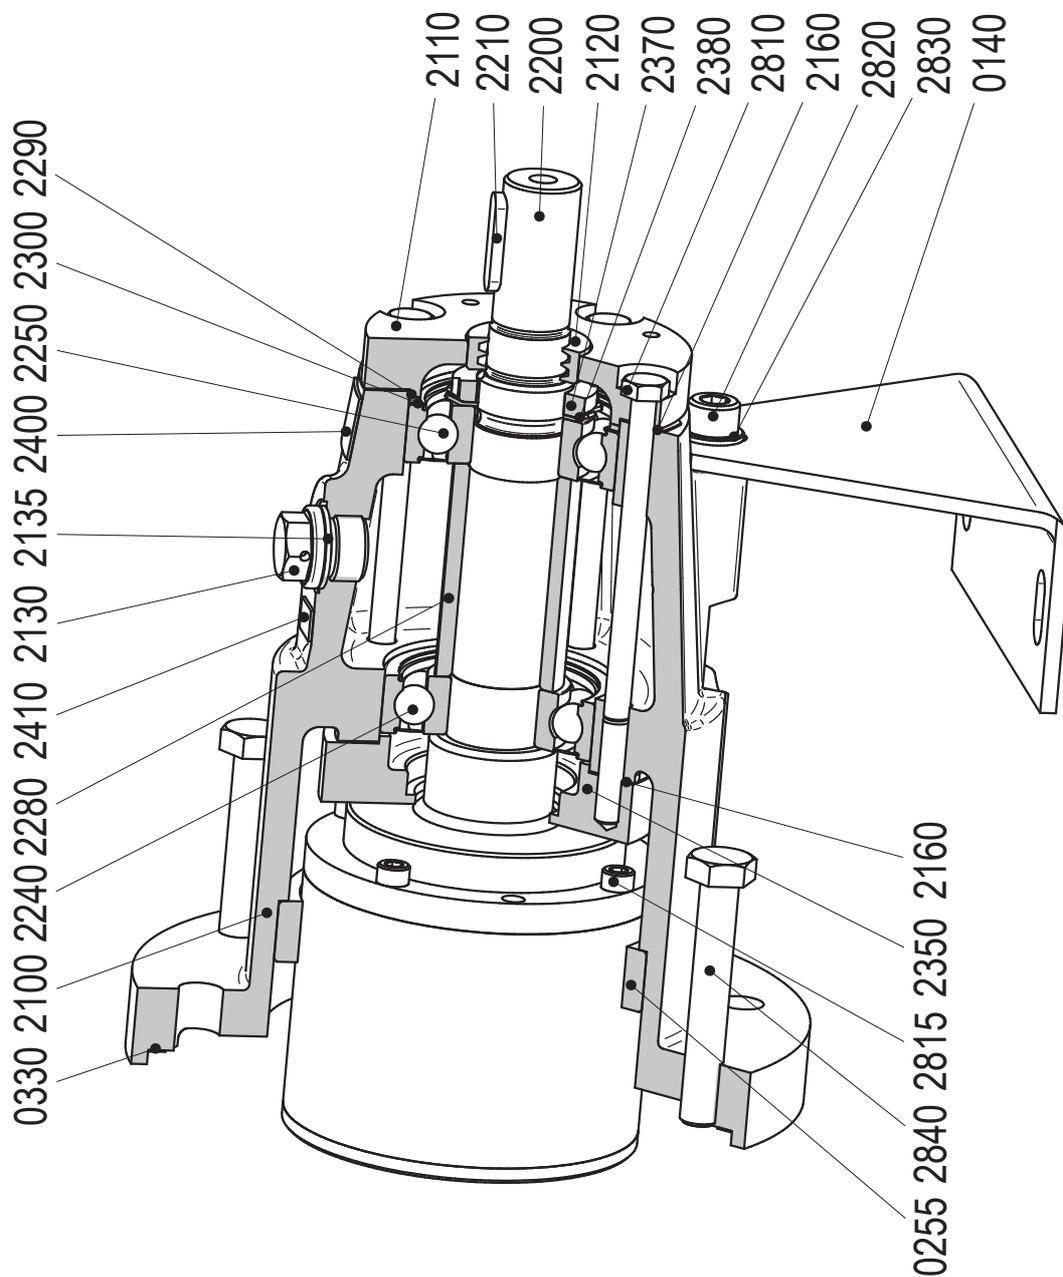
Роликовый подшипник L1 с консистентной смазкой, MAG 75
